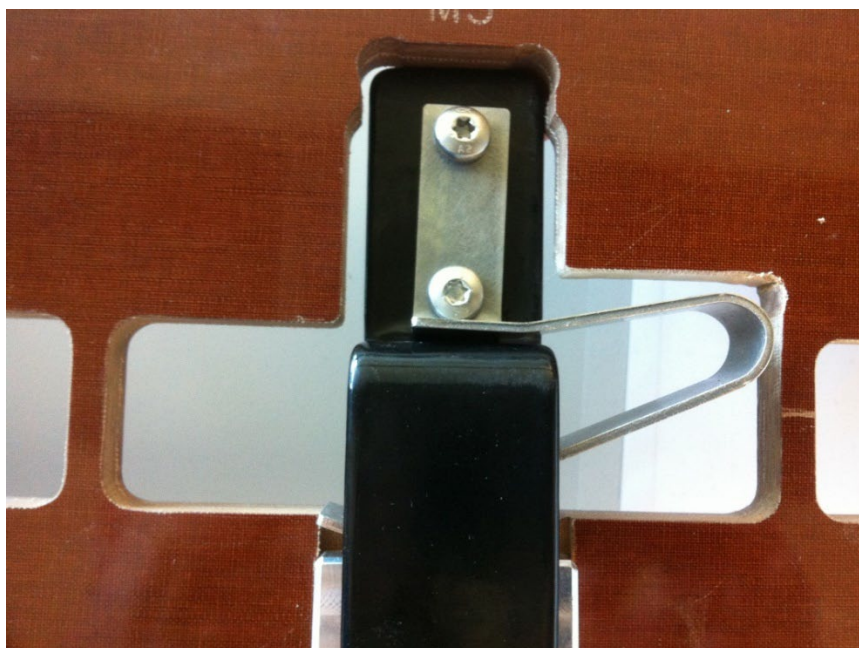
Gabarit de montage MegaSlate, découpe pour crochets milieu
